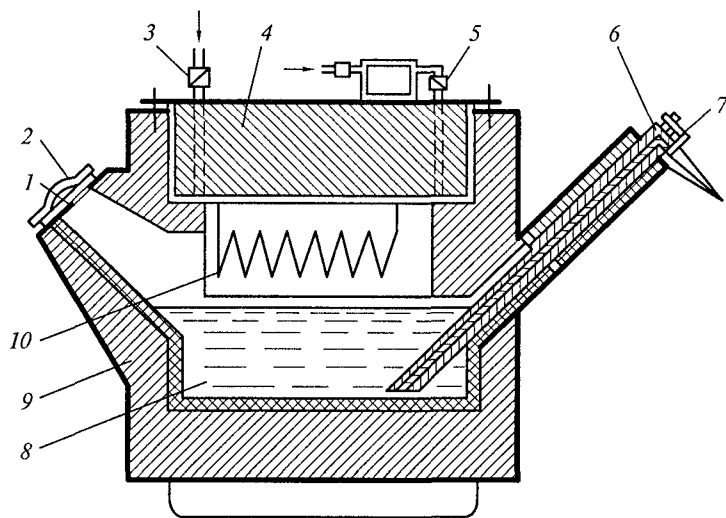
Пневматический дозатор для алюминиевых сплавов:
